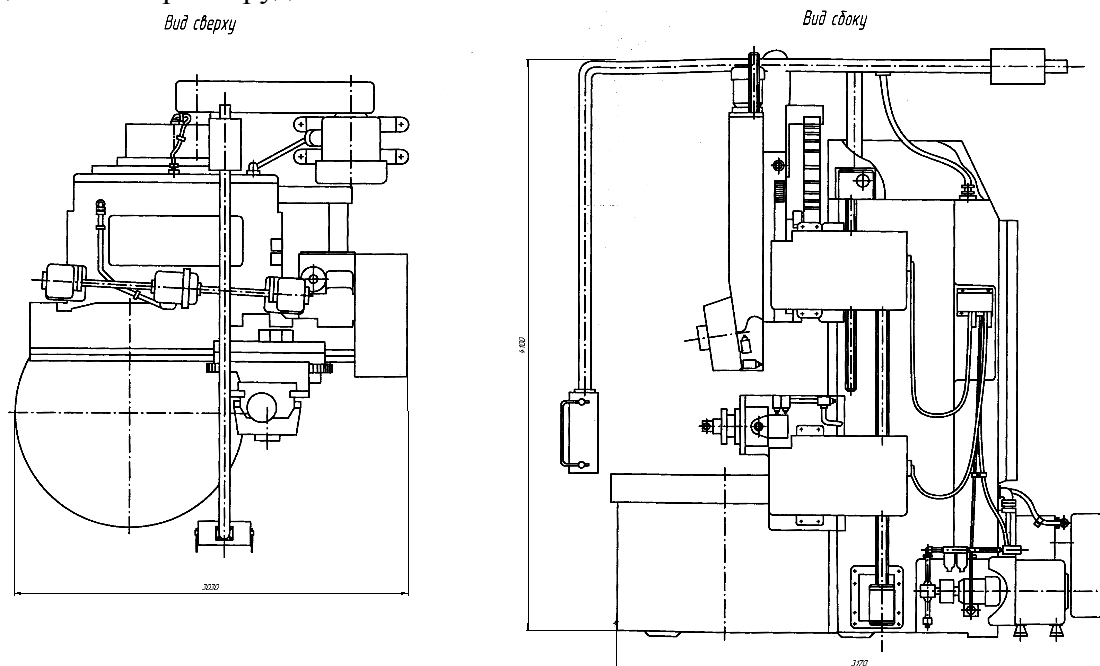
Общий вид токарно-карусельного станка 1516
